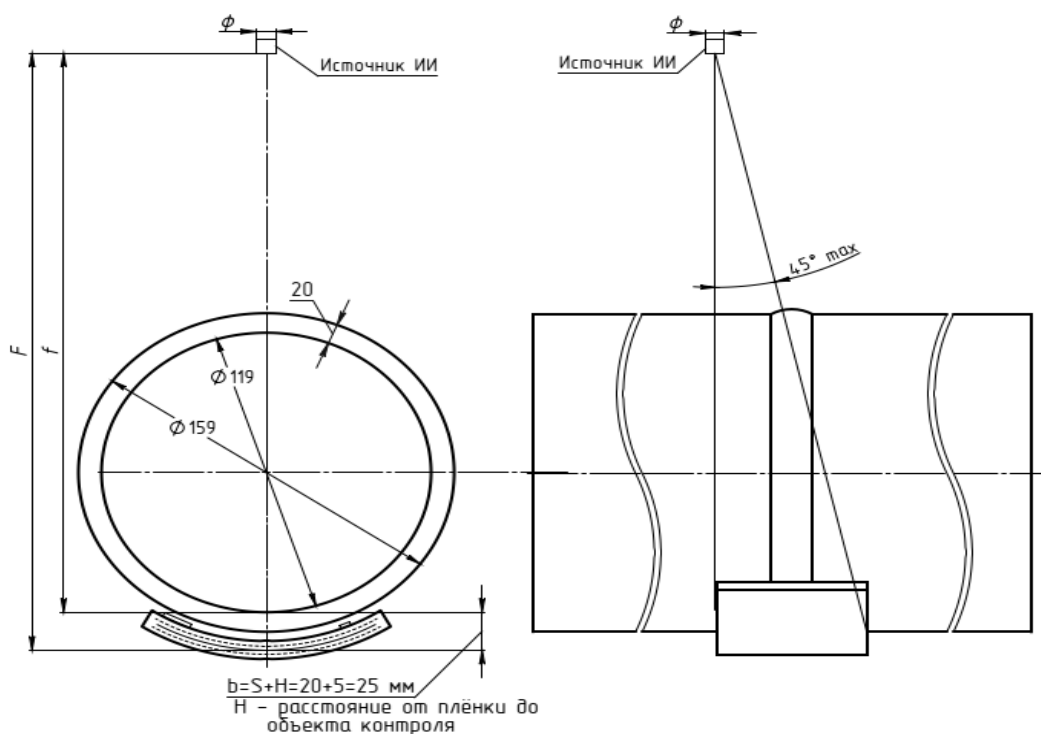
Схема контроля кольцевого сварного шва
